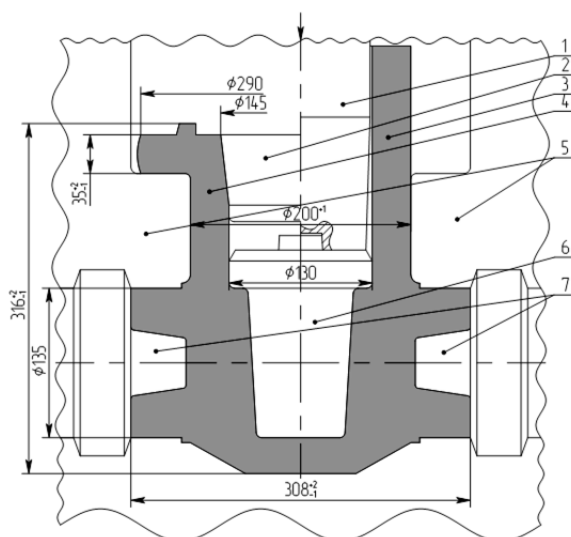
Схема штамповки корпуса ТД13075-100К1 из стали 12Х18Н10Т:
